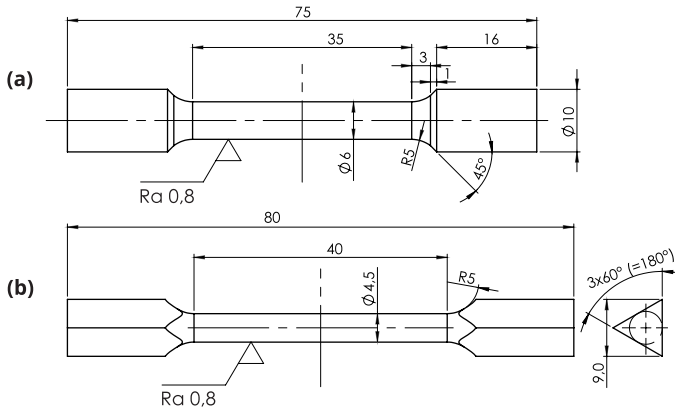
Geometriedefinition der geprüften Materialproben: (a) Zugprobe gemäß DIN EN ISO 6892-1 [148], (b) Torsionsprobe gemäß ASTM E143 [149]
